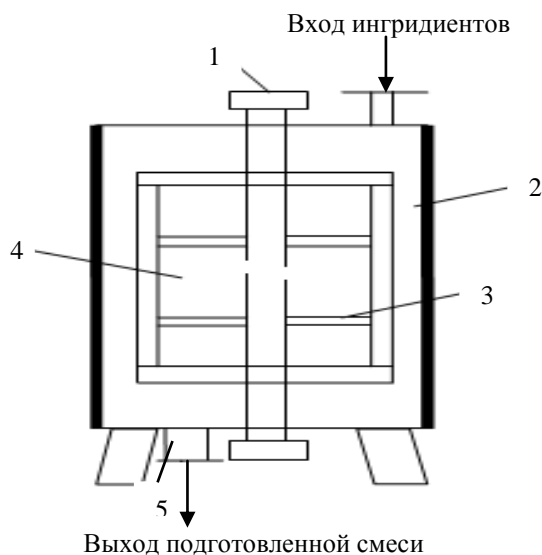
Аппарат для предварительной обработки (смешивания) жидких кормовых смесей
